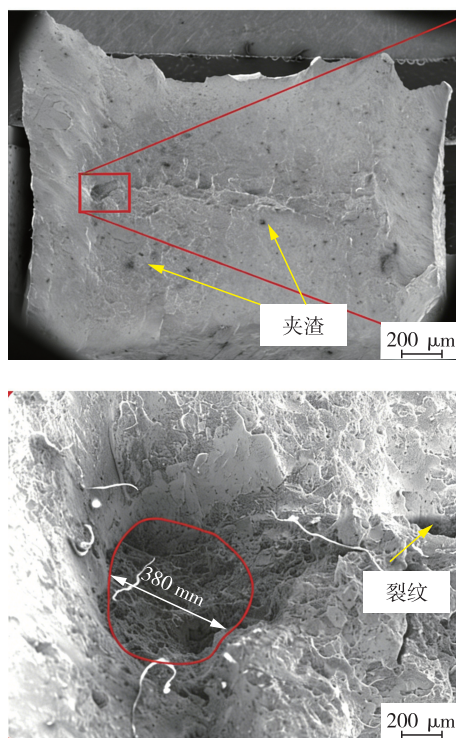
不加脉冲的焊缝拉伸断口形貌
